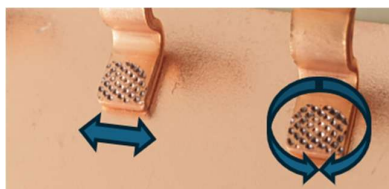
Inplane-Schwingungseinkopplung beim Ultraschall-Metallschweißen: a) linear, b) torsional
